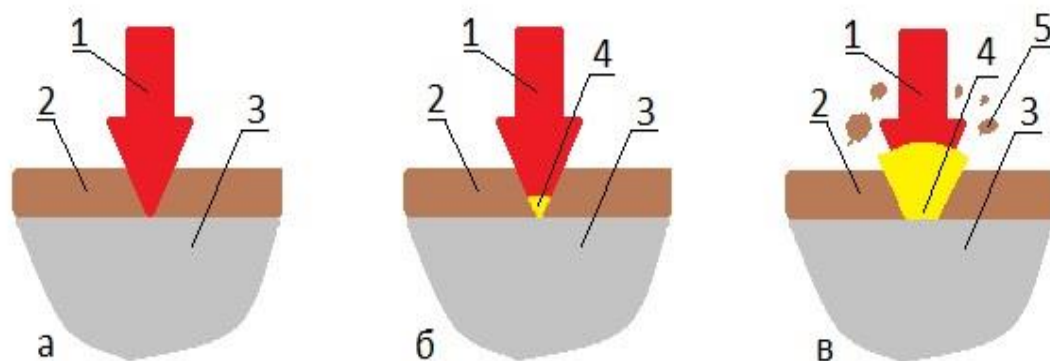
Испарительный механизм лазерной очистки колесных пар железнодорожного транспорта. 1 — лазерное излучение, 2 — загрязняющий материал, 3 — подложка, 4 — облако испаренного вещества, 5 — частицы загрязнения, удаляемые с поверхности подложки
